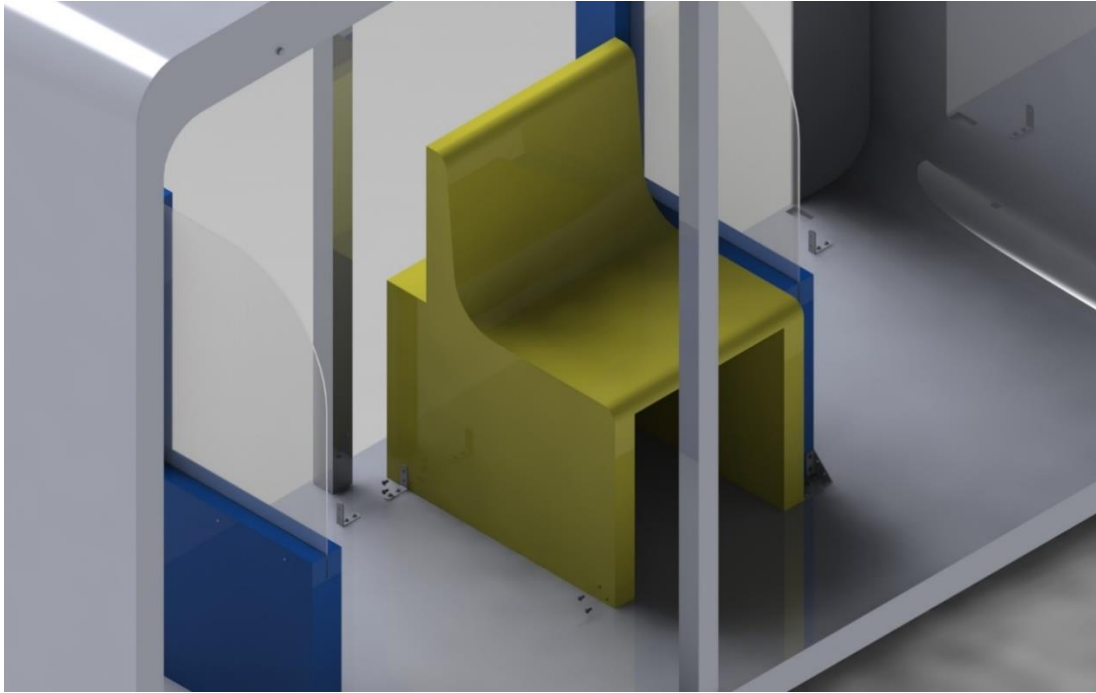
Ensamblaje conjunto. Unión escuadras y asiento.
